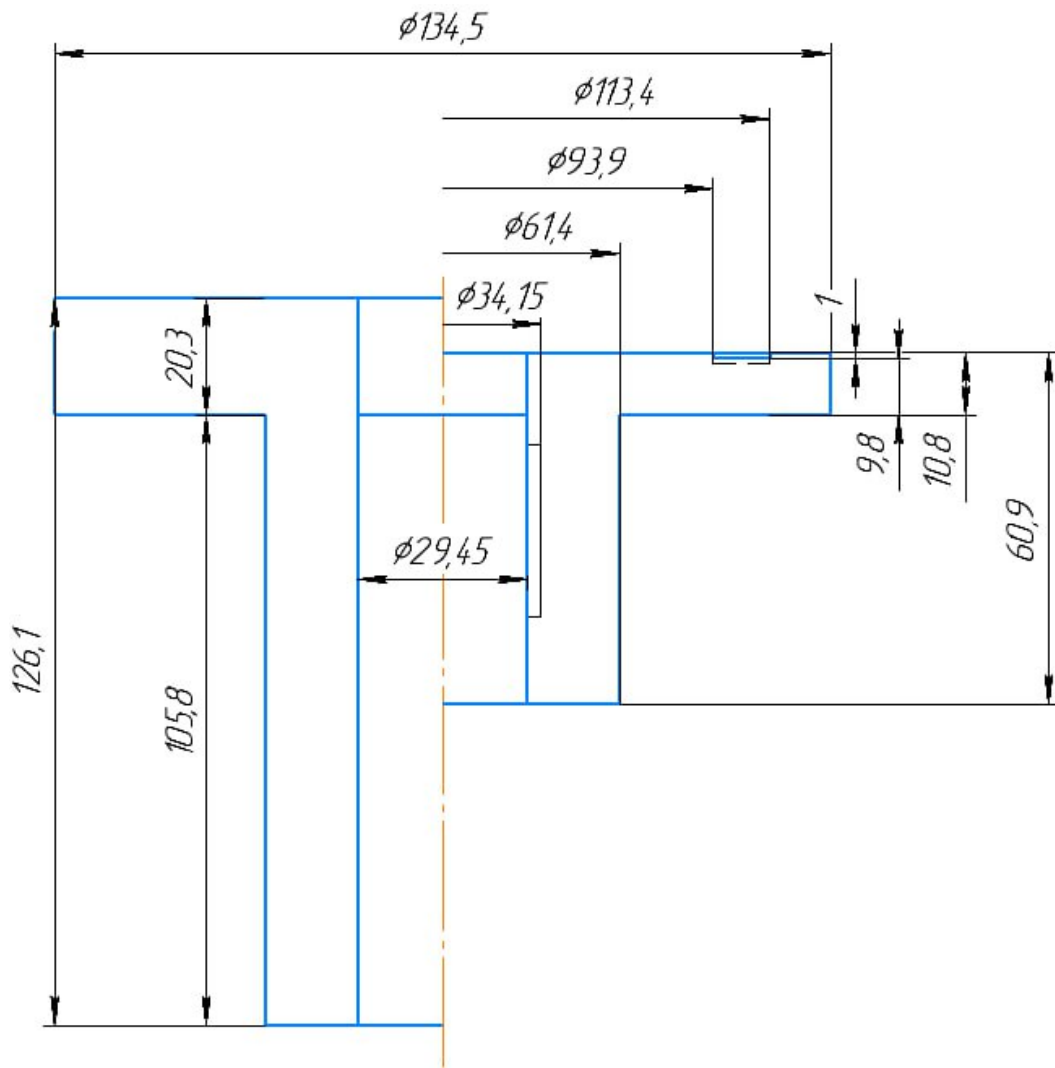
Размеры заготовки перед спеканием и размеры засыпки порошка в пресс-форме.
